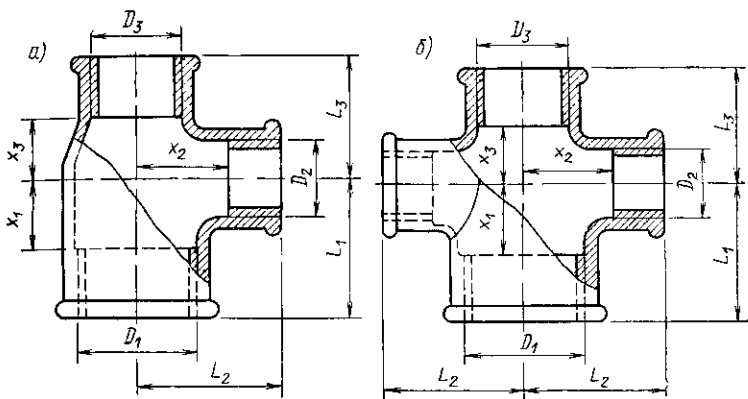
Соединительные части из ковкого чугуна (с двумя переходами)
